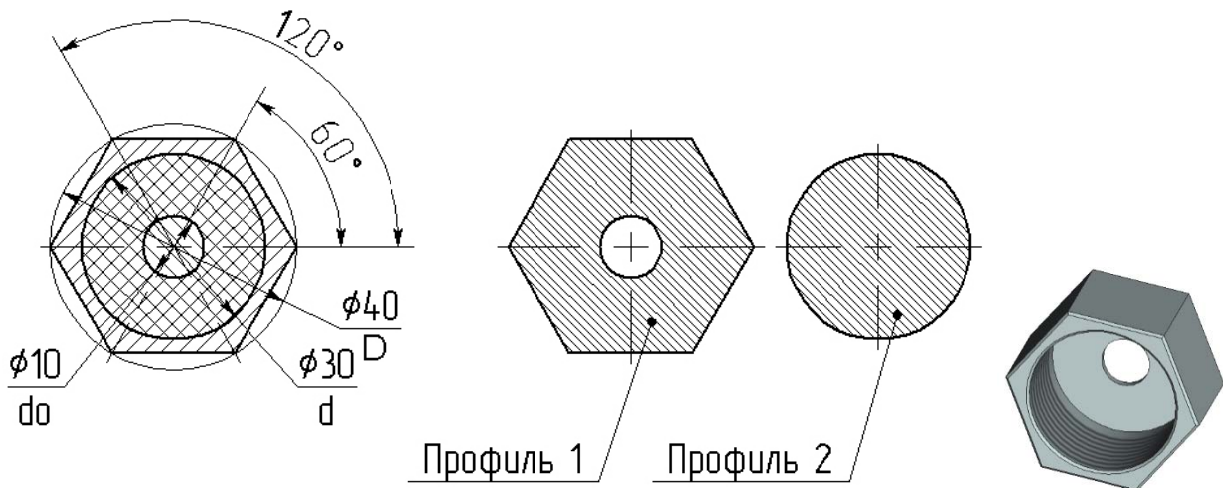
Чертеж и 3D модель детали «Гайка»
